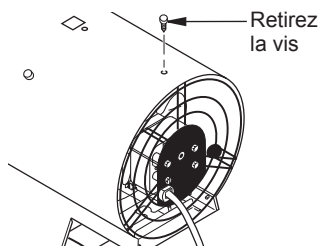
Retrait de la vis sur le dessus de la grille du ventilateur
